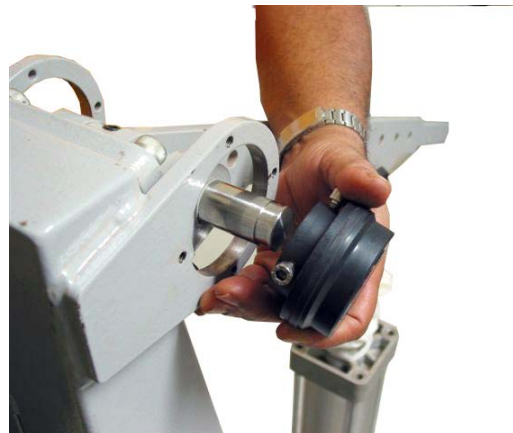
Suporte para Montagem e fixação do Ímã Rotativo
